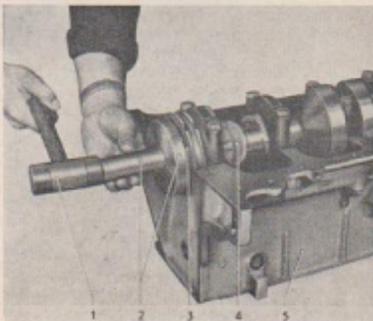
Wellendichtring für hinteres Kurbelwellenlager eintreiben
